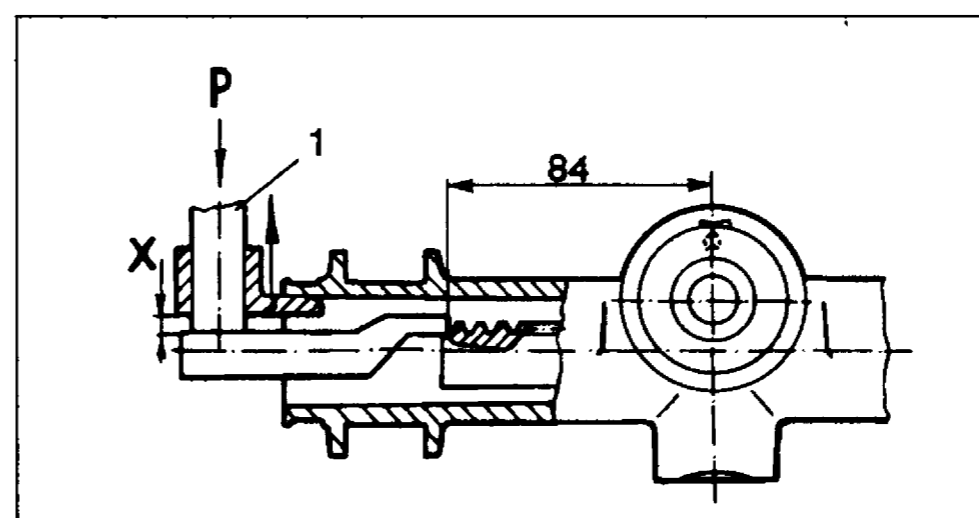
Проверка зазора между упором рейки и гайкой:
